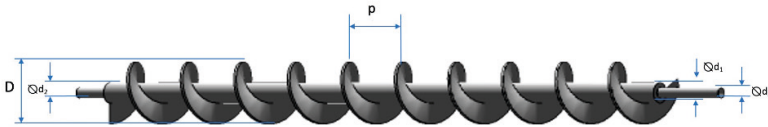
Dimensiones principales de la hélice de un tornillo sin fin.
